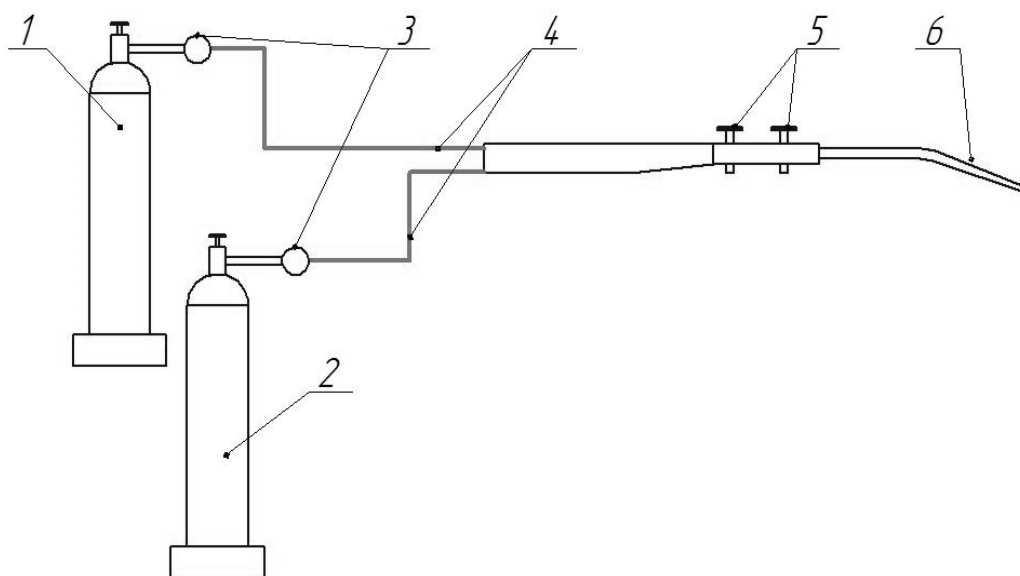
Схема устаткування для порошкового напилювання:
